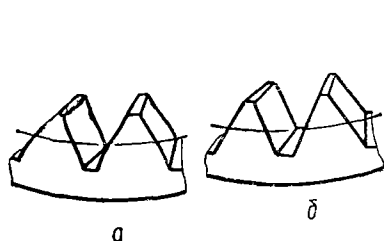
Торцовое сечение зубьев производящего колеса
